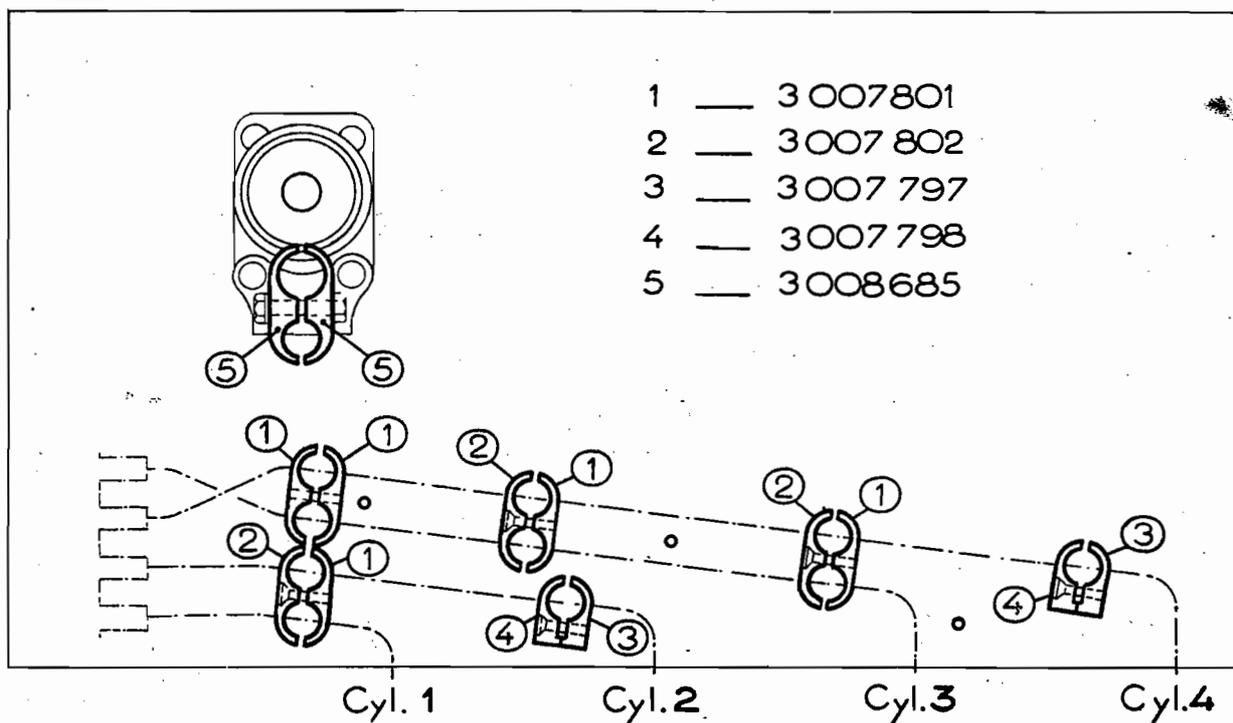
MONTAGE DES TUBES DE DÉMARRAGE
